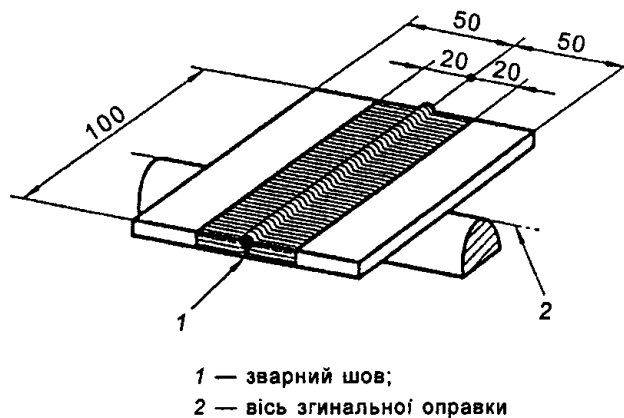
Випробний зразок листів і стрічок зі стиковими швами
